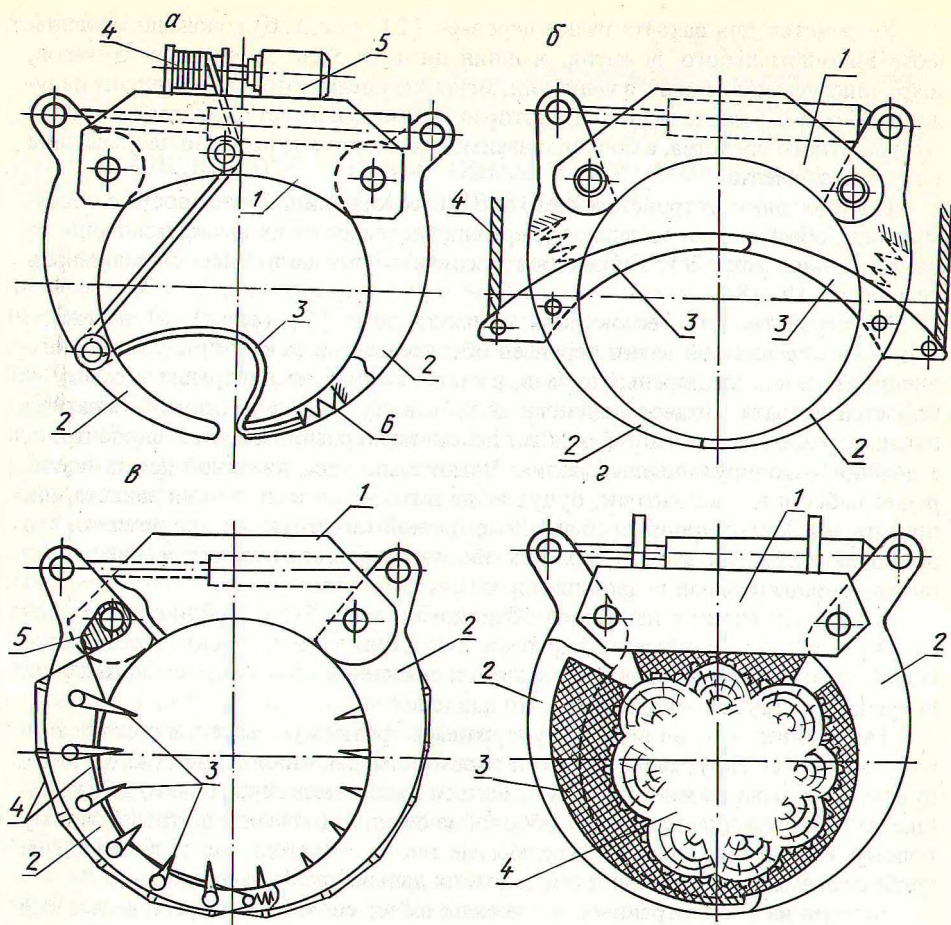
Конструкции пачковых захватов для бесчокерной трелевки леса:
